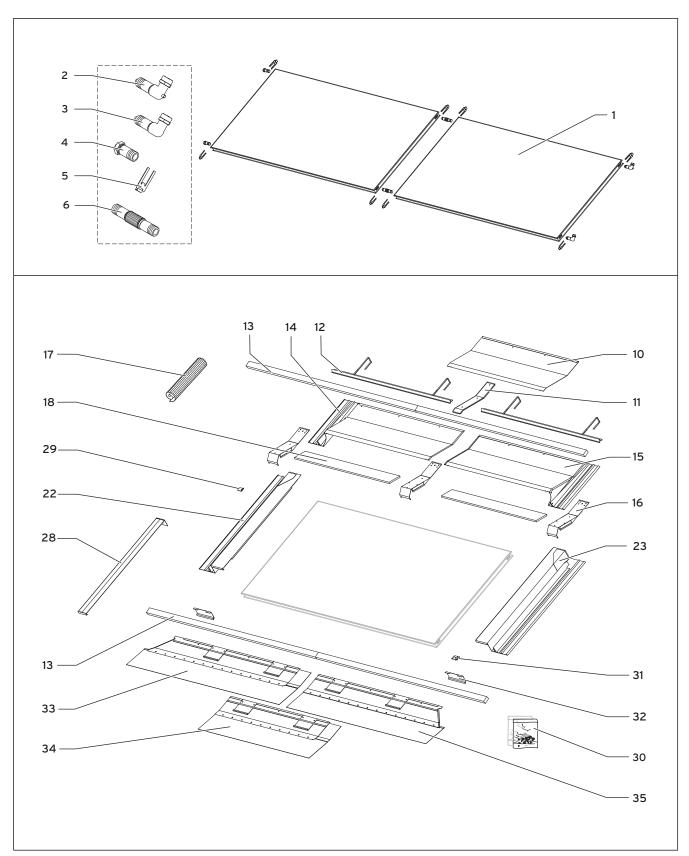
Kit de montaje del colector horizontal (VFK 145/2 H)
